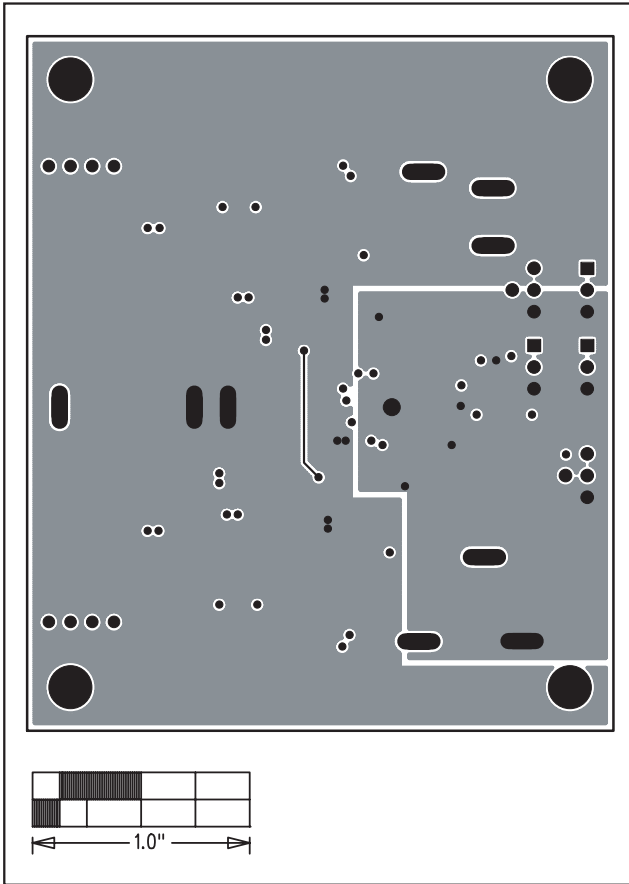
MAX1540 评估板 PCB 布局 – 接地层 3
